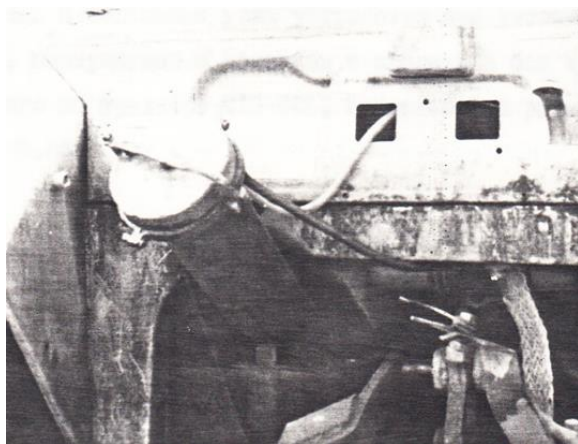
Топливный бак с закрытой герметизирующей крышкой
